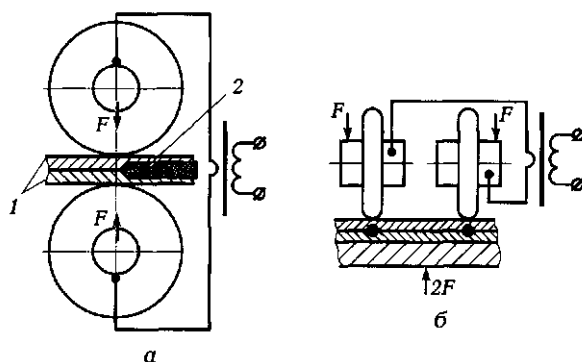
Роликовая (шовная) сварка:
